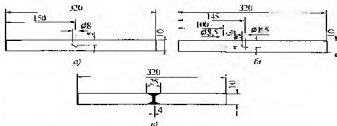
Схема сверления отверстий (а) и сварки образцов (б)
